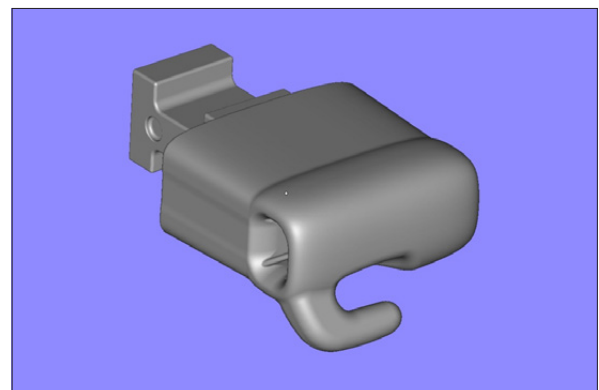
Tube in der Langversion mit einem zusätzlichen Haken, der einzig als Attachment für Gummiketten dient.
